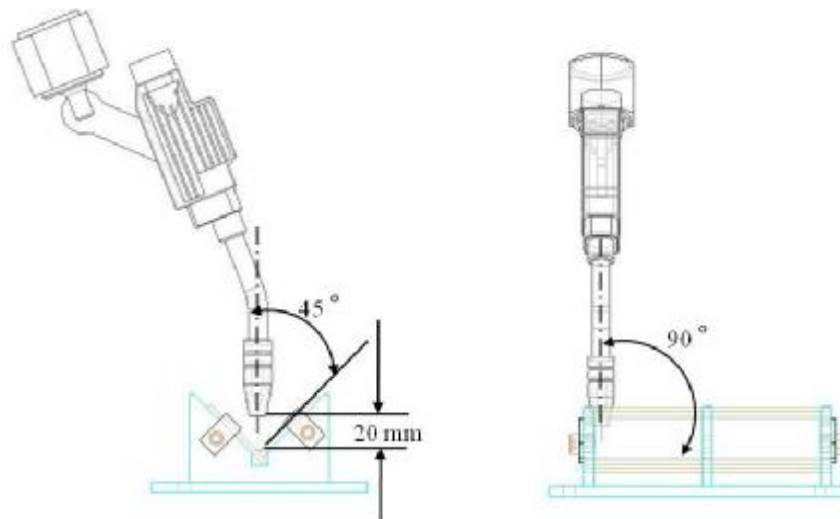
Posição da tocha de soldagem em relação ao eixo do cordão de solda.
